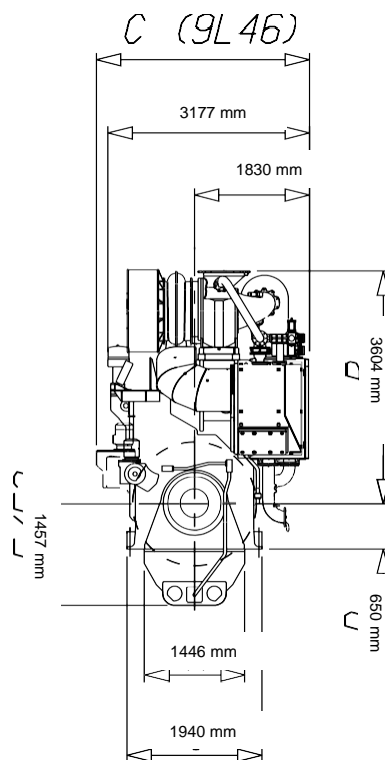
Dimensiones frontales del motor Wärtsilä 8L46C. “Wärtsilä, Marine Project Guide W46 - 1/2001”
